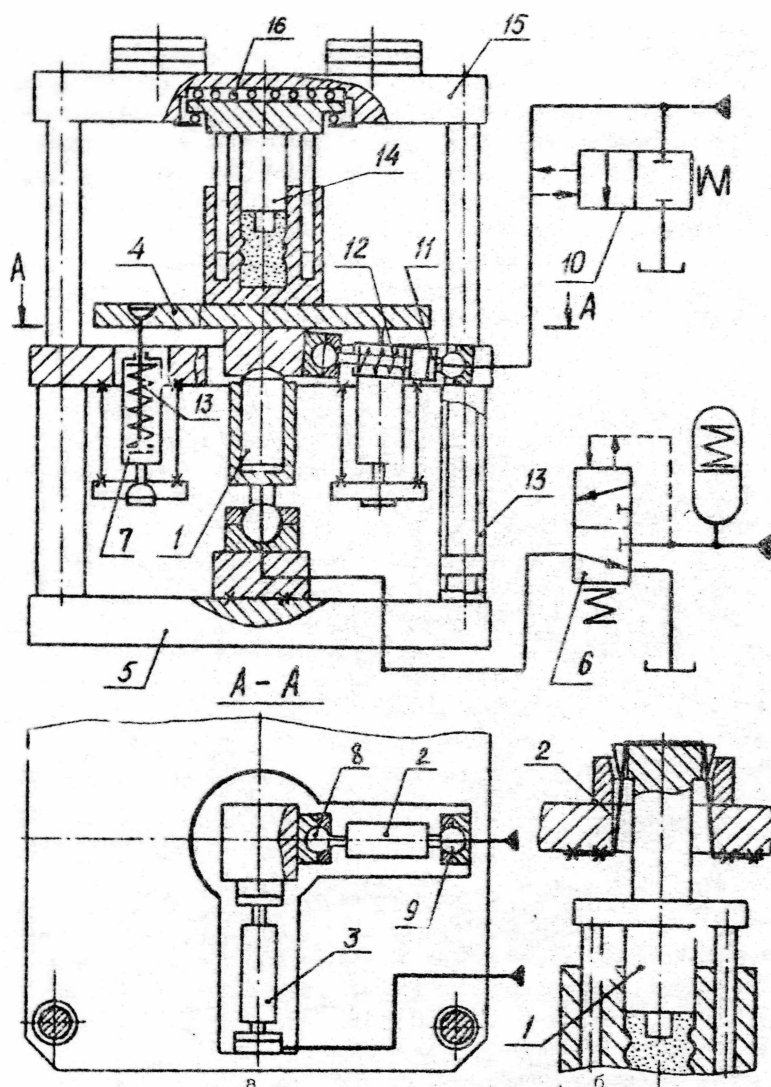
Конструктивная схема вибропресса с трехкоординатным движением рабочего стола - а и устройства для разгрузки п. нсопа в горизонтальном направлении - б.
